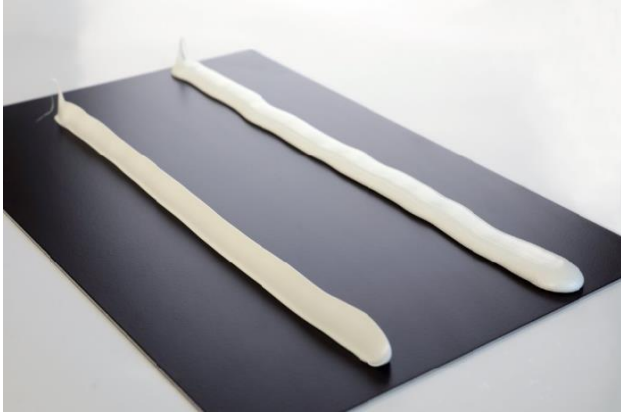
Aufgetragene Klebstoffraupe (dreieckige und runde Form)
